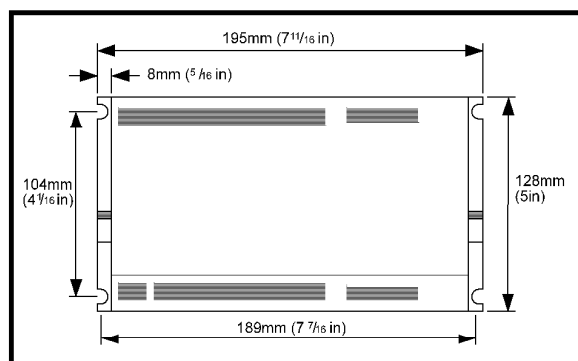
Montaggio del Box I/O su sbarra DIN
